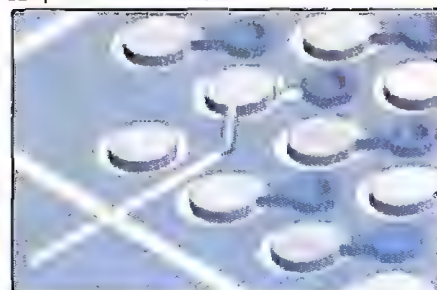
Удалить площадку BGA и отфрезеровать неглубокую канавку в поверхности паяльной маски
